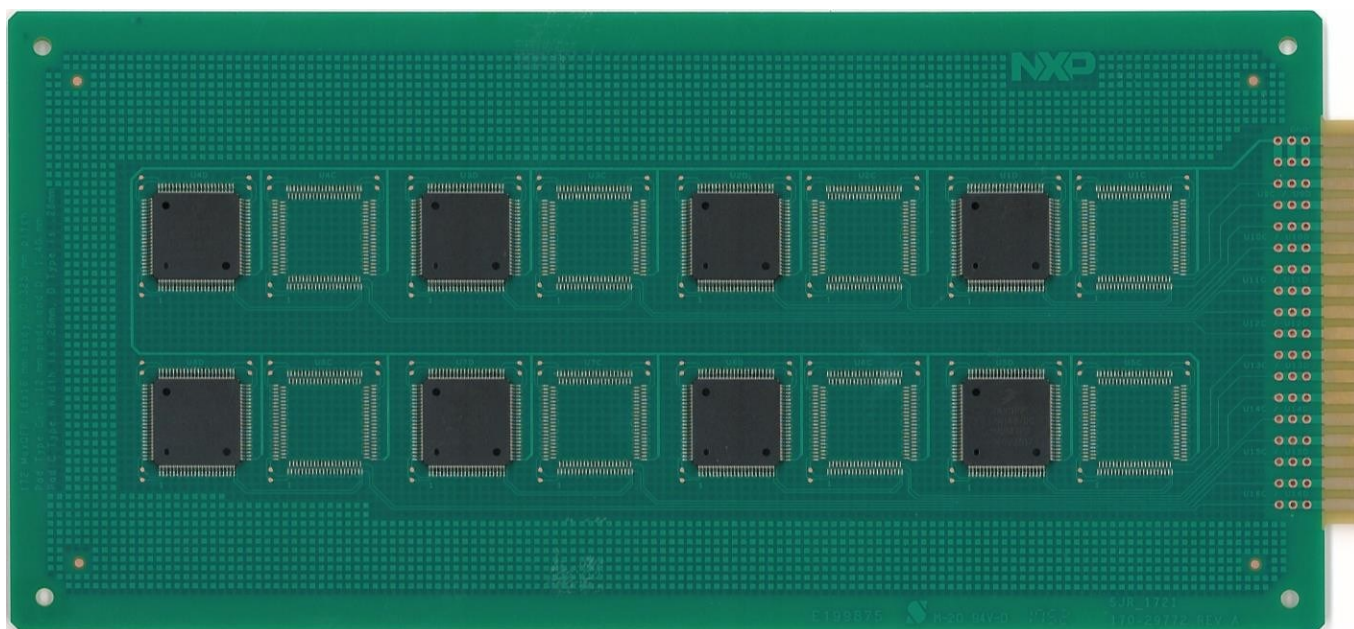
用于板级可靠性测试的 172 MaxQFP PCB
